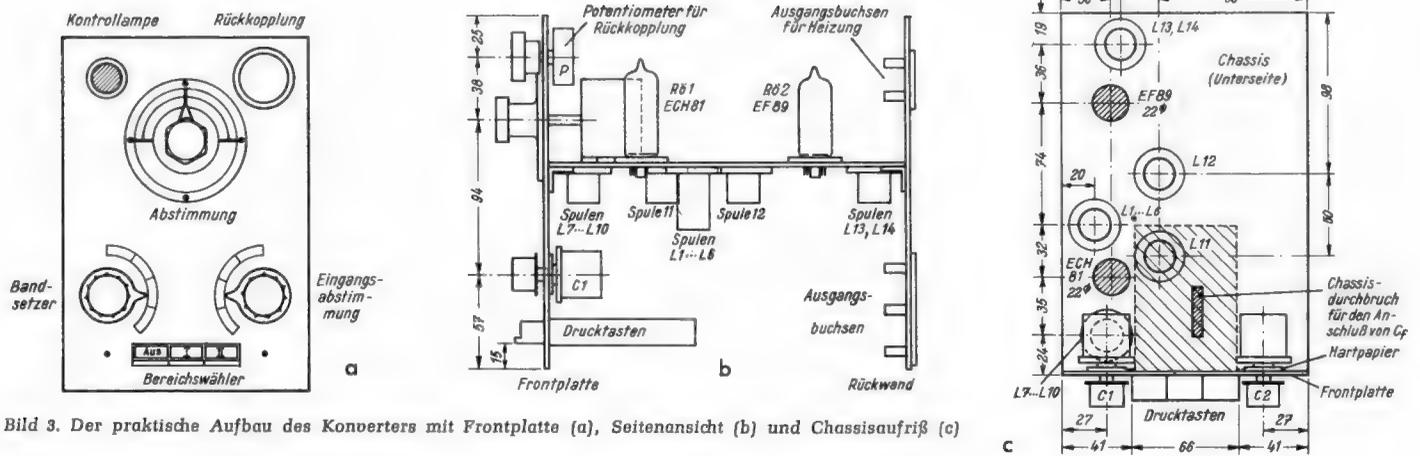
Der praktische Aufbau des Konverters mit Frontplatte (a), Seitenansicht (b) und Chassisaufriß (c)
